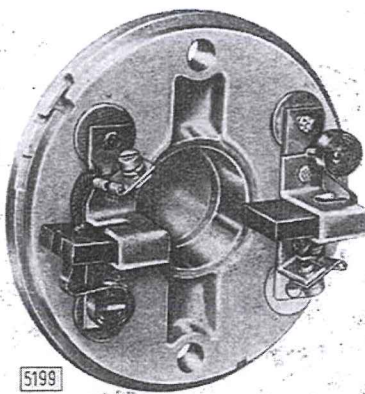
Supporto lato collettore completo di spazzole di cui una con la molla puntata sul fianco per facilitare le operazioni di smontaggio e rimontaggio.
